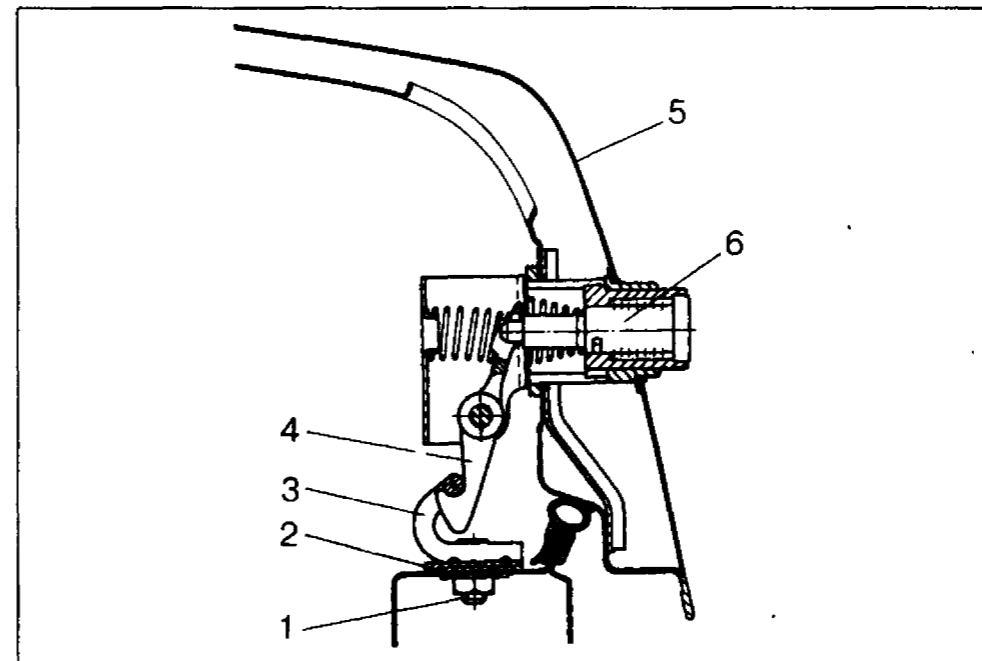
Замок крышки багажника: 1 — болт крепления фиксатора; 2 — регулировочная прокладка; 3 — фиксатор; 4 — крючок; 5 — крышка багажника; 6 — кнопка с личинкой замка
